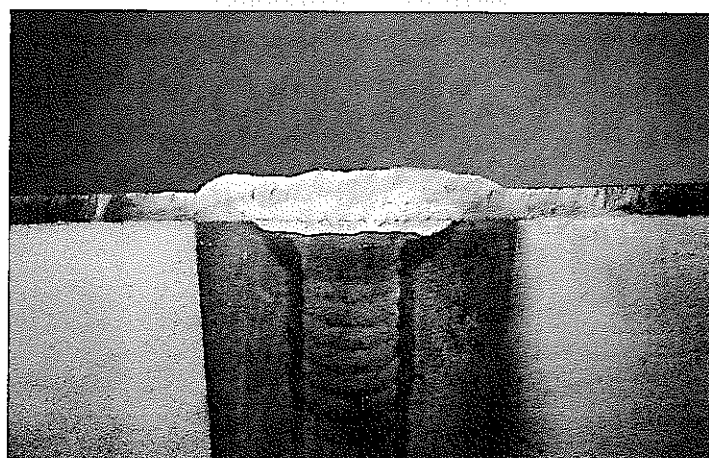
蓋部溶接部への最終チタン被覆施工
